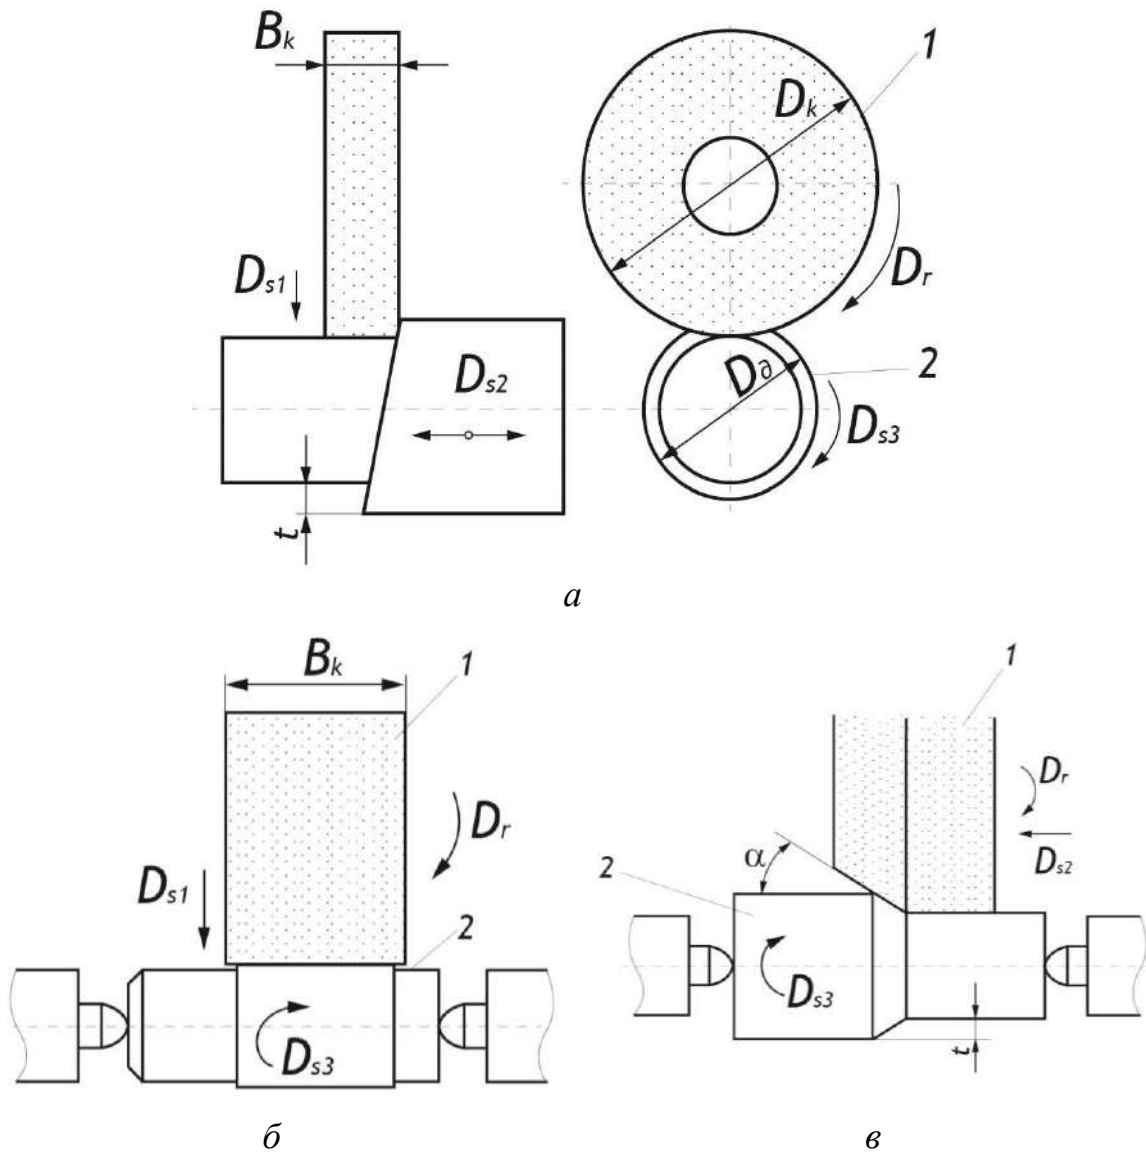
Способи круглого зовнішнього шліфування: *а* – шліфувальний круг, *б* – оброблювана заготовка, *в* – глибоке шліфування
